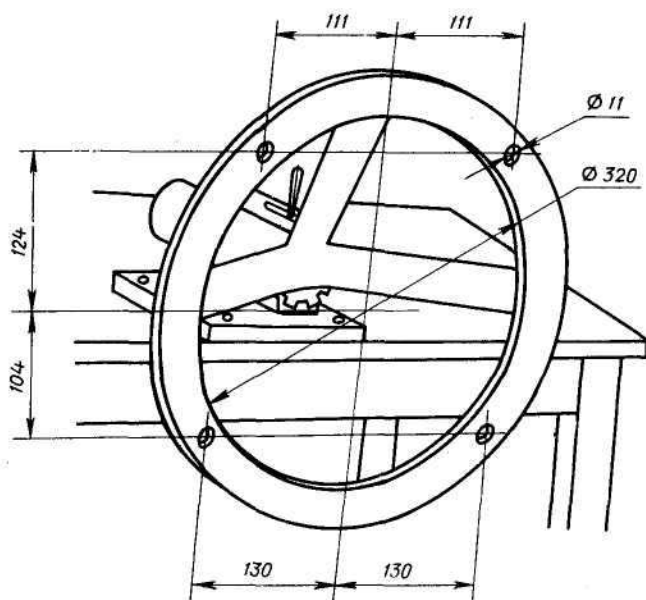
Приспособление для крепления двигателя при разборке и сборке
